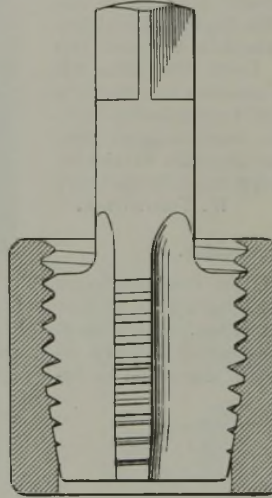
Gewindebohrer mit Flankenschnitt für Whitworth-Rohrgewinde.
